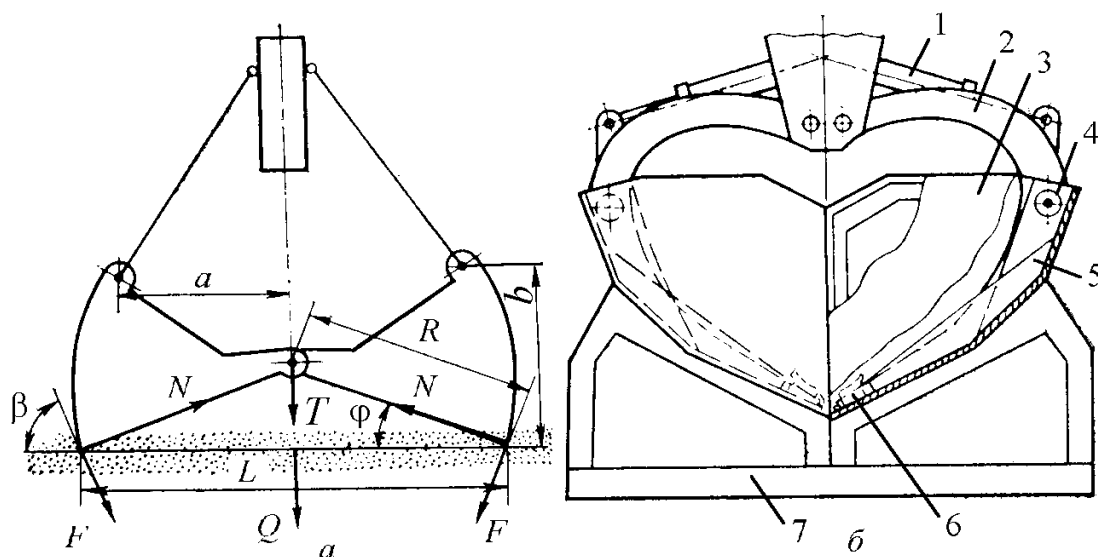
Ковшовый грейфер: *a* – расчетная схема; *б* – ковшовая насадка для радиального грейфера: 1 – гидроцилиндр; 2 – челюсть радиального грейфера; 3 – полуковш насадки; 4 – поворотный замок оси крепления; 5 – направляющие челюстей; 6 – проушина; 7 – подставка для насадки
